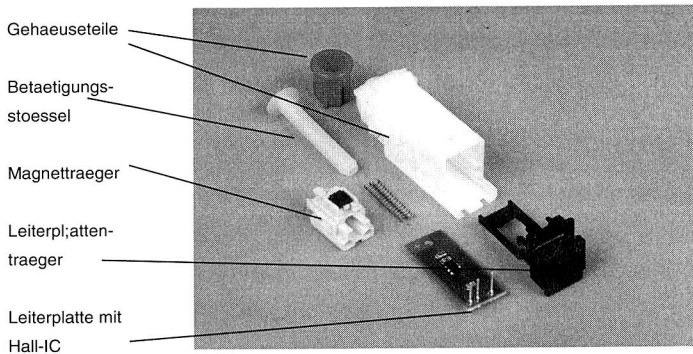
Bremslichtschalter in mechanischer, konventioneller Aufbautechnik
